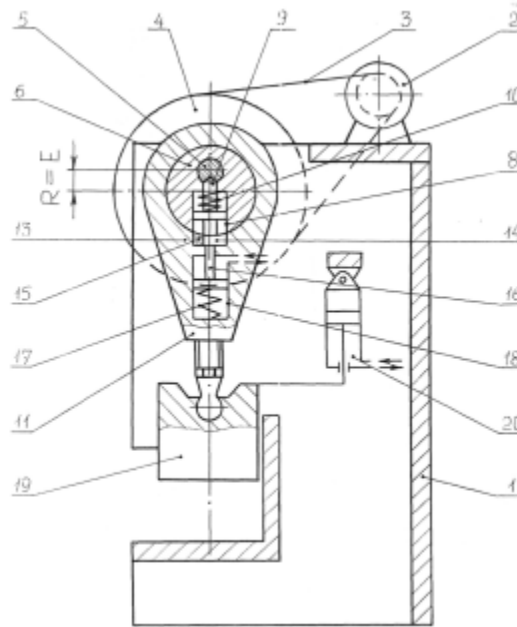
Загальний вигляд кривошипного безмуфтового преса з циліндричним фіксатором
